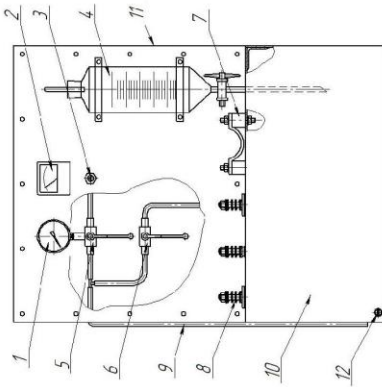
Установка для очистки топливных систем автомобилей марки КС-120
